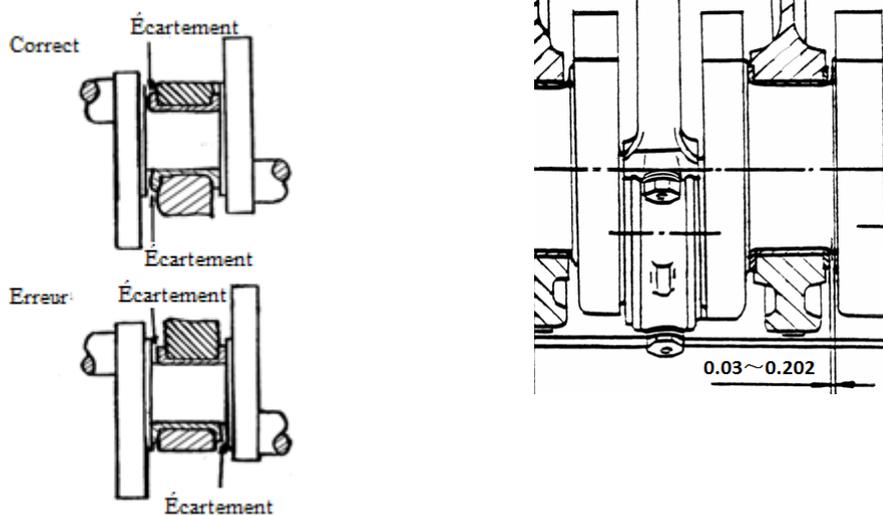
Ensemble vilebrequin-plaque de poussée
